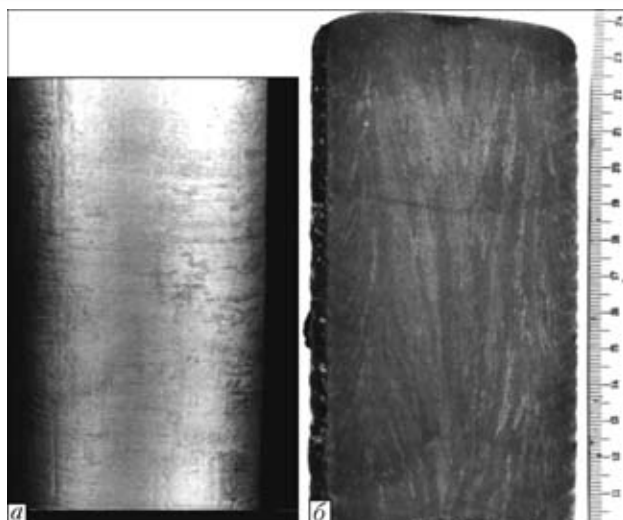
Внешний вид (а) и макрошлиф (б) продольного сечения слитка стали Р6М5, полученного переплавом стружки быстрорежущей стали
